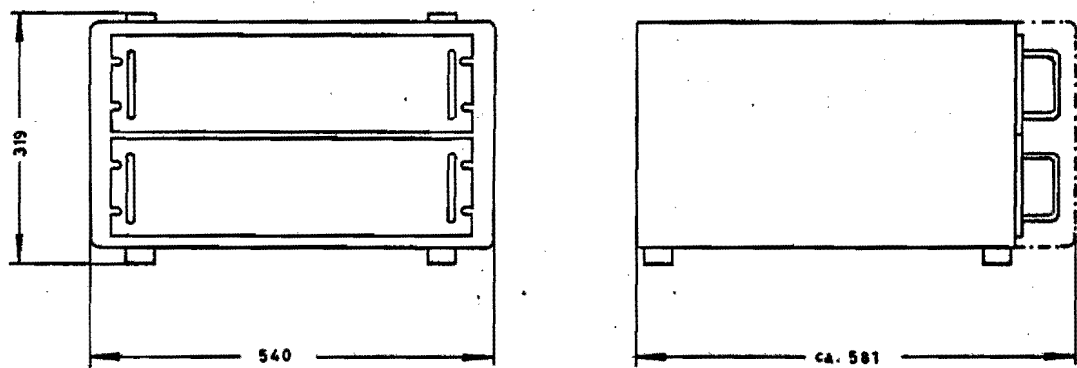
Abmessungen in mm des gemeinsamen Gerätekastens
